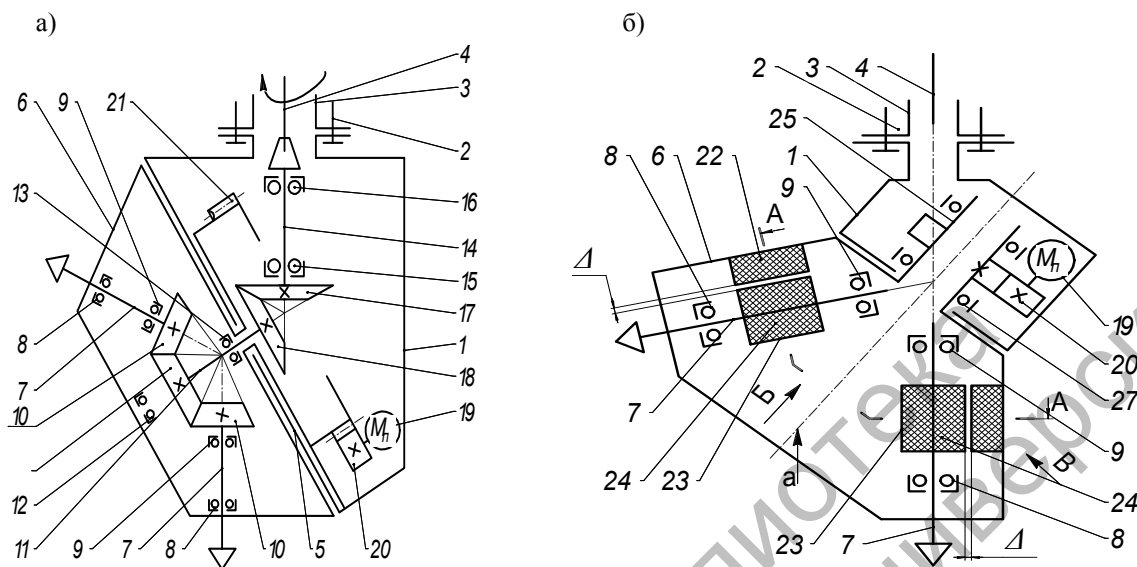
Головка револьверная (настоящее) (а) и мотор-головка револьверная (будущее) по патенту Украины № 109191 с генетической формулой  $[КН\ 0.2y]_1 \times [пЦЛ\ 0.2y]_2$  (б); 1 – корпус; 2 – болты; 3 – шпиндельный узел станка; 4 – ось шпинделя станка; 5 – нижний торец корпуса; 6 – поворотная планшайба; 7 – рабочие инструментальные шпиндели; 8, 9 – передние и задние опоры рабочих шпинделей; 10 – конические зубчатые колеса на концах шпинделей 7; 11, 18 – центральные конические зубчатые колеса на приводном валу; 12, 13 – опоры приводного вала; 14 – центральный вал на опорах; 17, 18 – зубчатая коническая пара; 19 – электродвигатель поворота планшайбы; 20, 21 – цилиндрическая зубчатая пара; 22 – статор конусообразной формы; 23 – якорь вращательного движения с обмотками; 24 – обмотки; 25 – хвостовик планшайбы на опорах; 26, 27 – опоры
